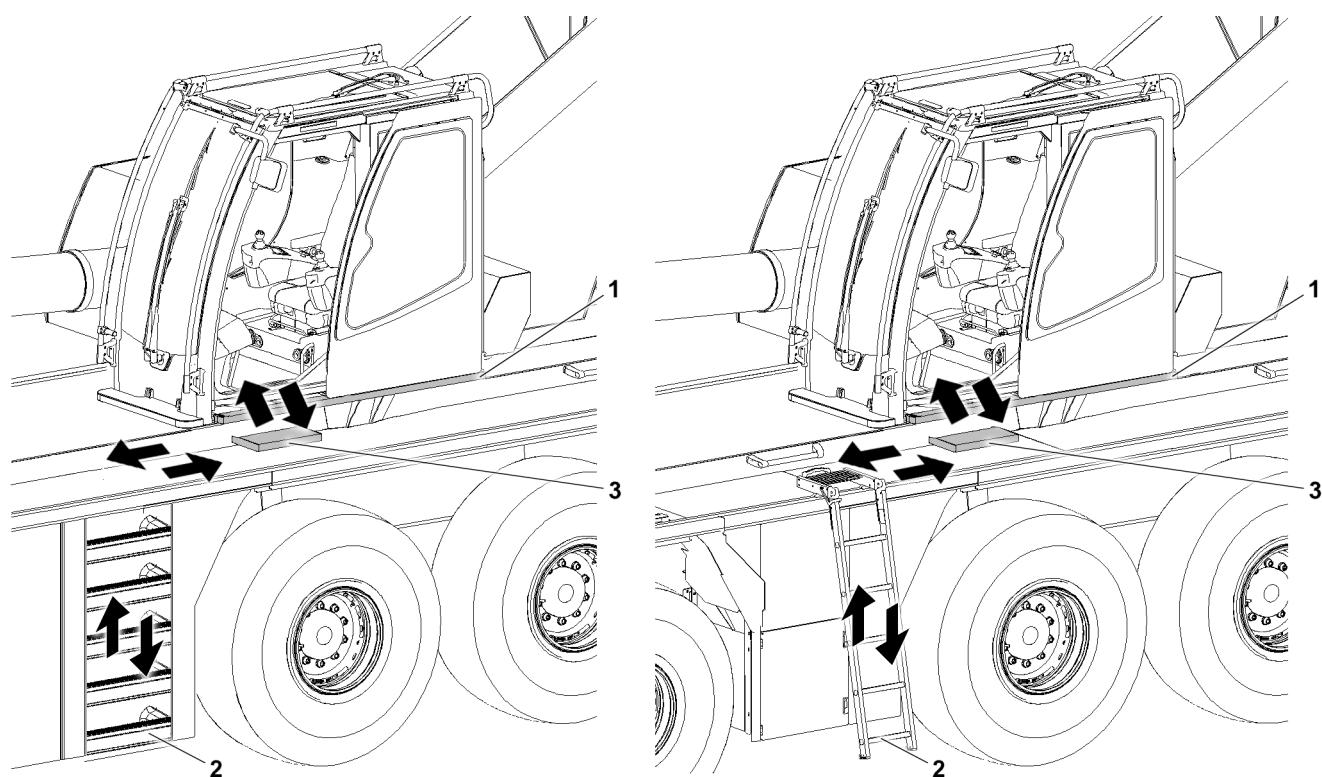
Superestructura en posición de 180°: Peldaño retraído
